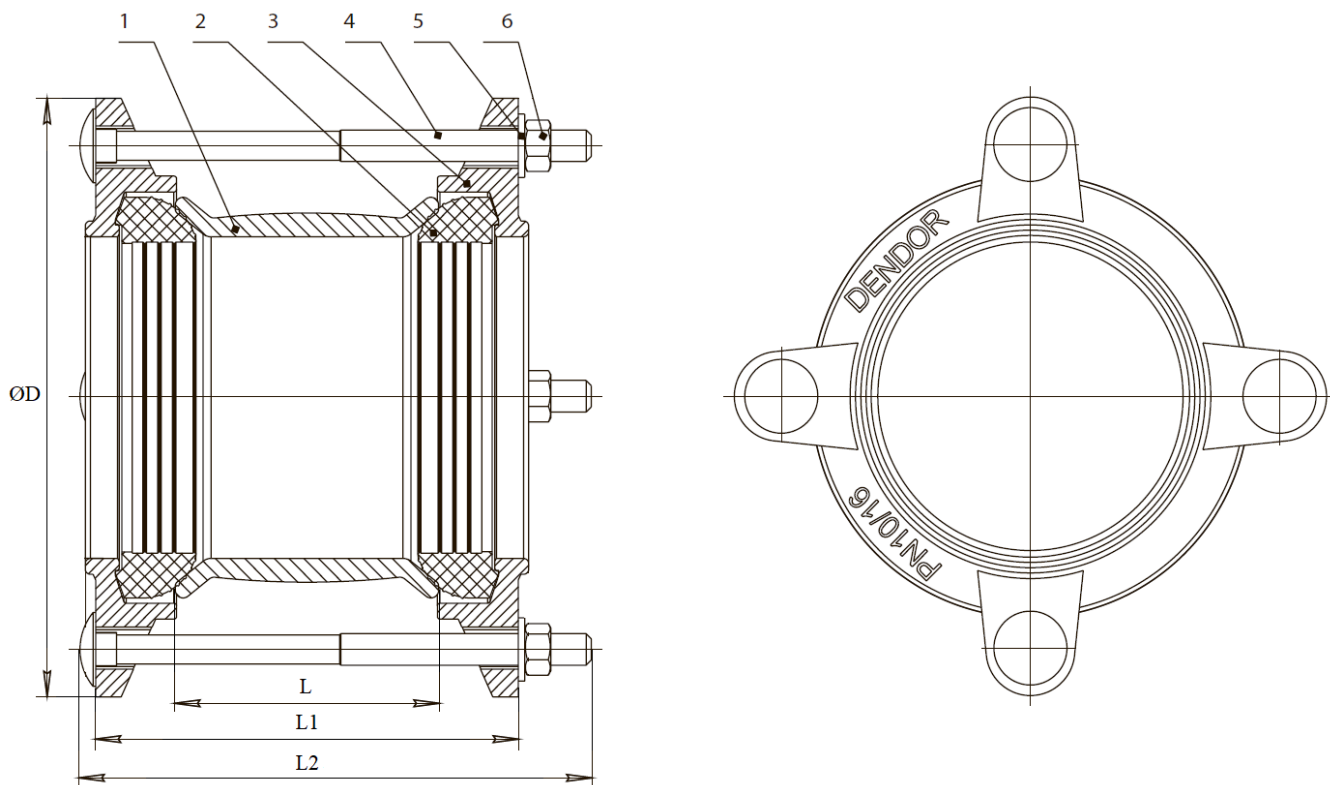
Муфта соединительная универсальная RC-U13.J DN50-700 PN16 и муфта соединительная RC-U13.J FIX DN800-2000 PN16
